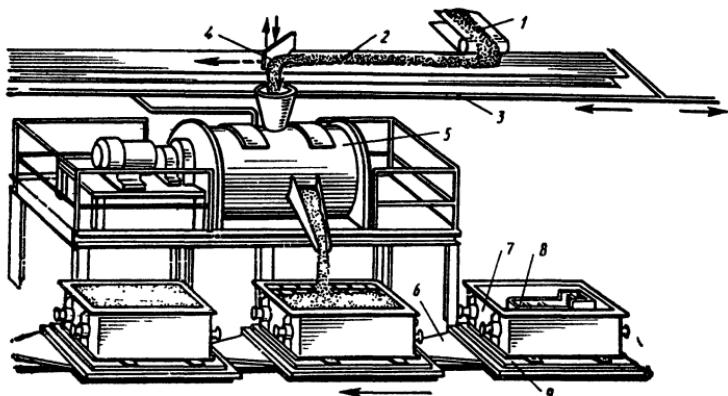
Общий вид стационарной установки периодического действия для изготовления форм из ЖСС при получении отливок массой до 1,5 т:
